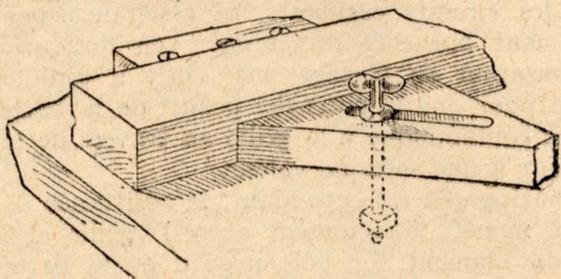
Equerre de serrage fixée par un écrou passant dans une coulisse.
